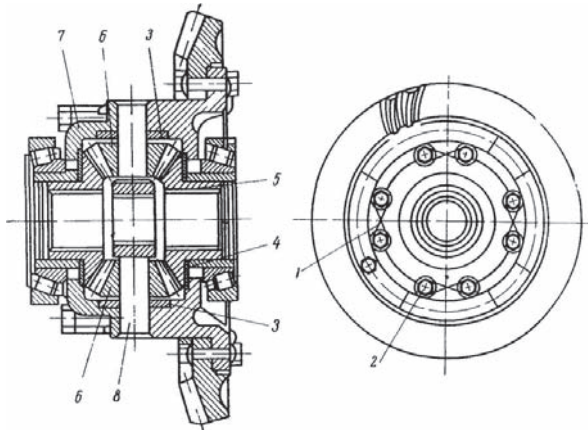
Дифференциал в сборе. 1 — контрольная проволока; 2 — болты; 3 — опорная шайба сателлита; 4 — опорная шайба полуосевой шестерни; 5 — полуосевая шестерня; 6 — сателлит; 7 — крышка; 8 — крестовина.
